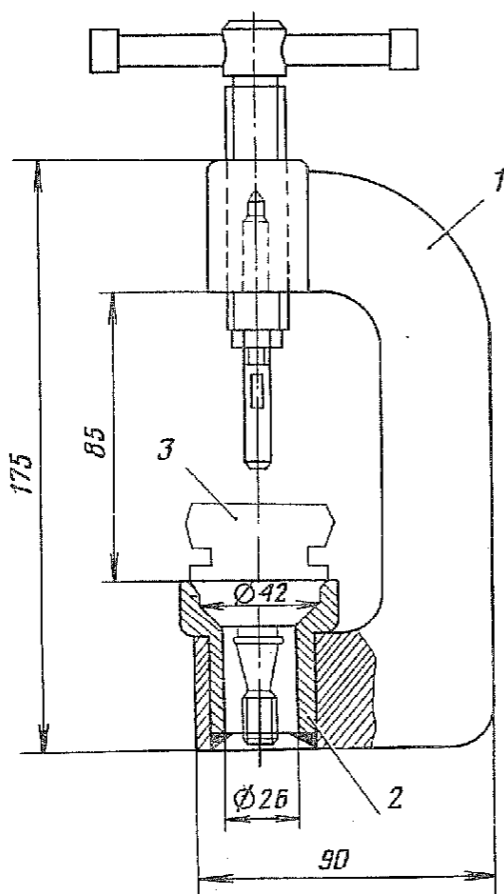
Приспособление для разборки и сборки шаровых шарниров:
